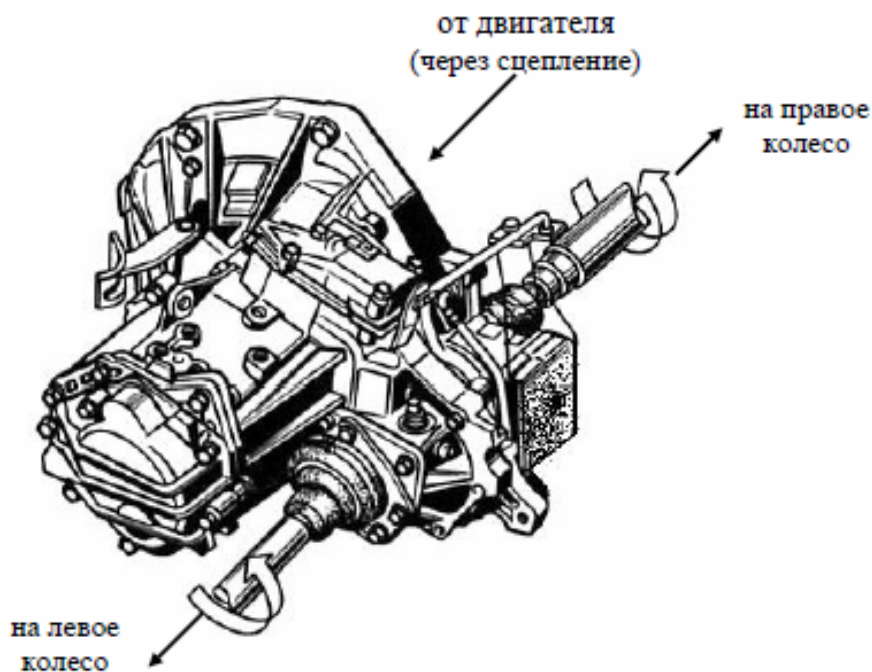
Общий вид двухвальной коробки передач переднеприводного легкового автомобиля при поперечной установке силового агрегата
